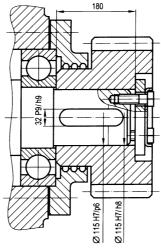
Установка шестерни на цилиндрическом конце вала
